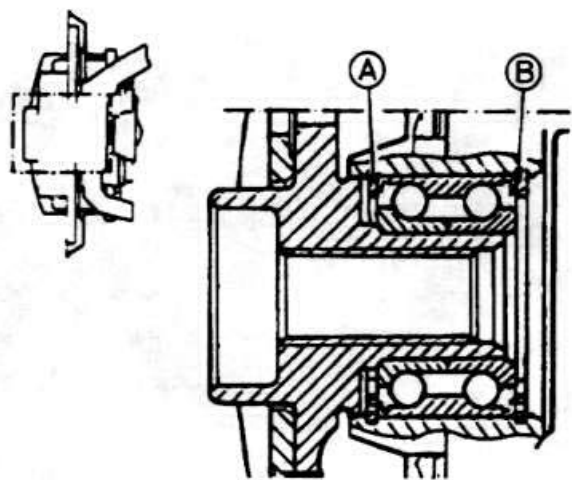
Сборка ступица/подшипник переднего колеса:
